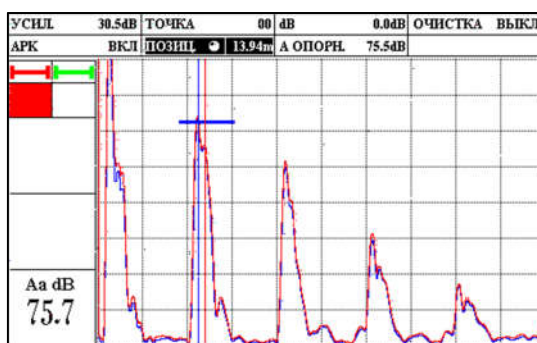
Установка позиции второй опорной точки АРК
